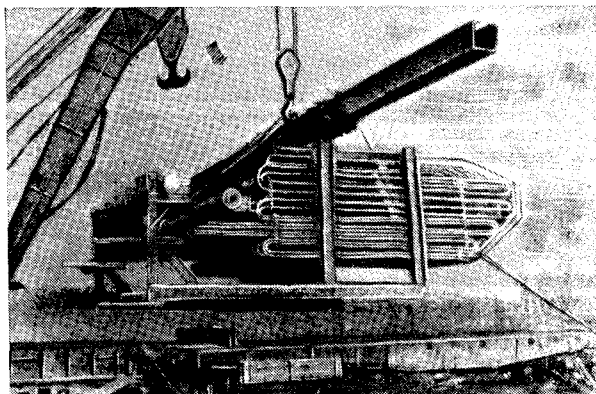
Блок выходного пакета пароперегревателя со специальным приспособлением для сборки.
